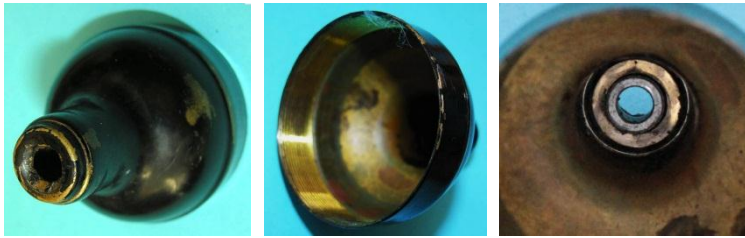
Befestigung des Drehbolzens: a) Spannmutter innerhalb des Gehäuses, b) Ring mit Arretierungsnut, c) Drehbolzen mit Spannmutter und Nutring
